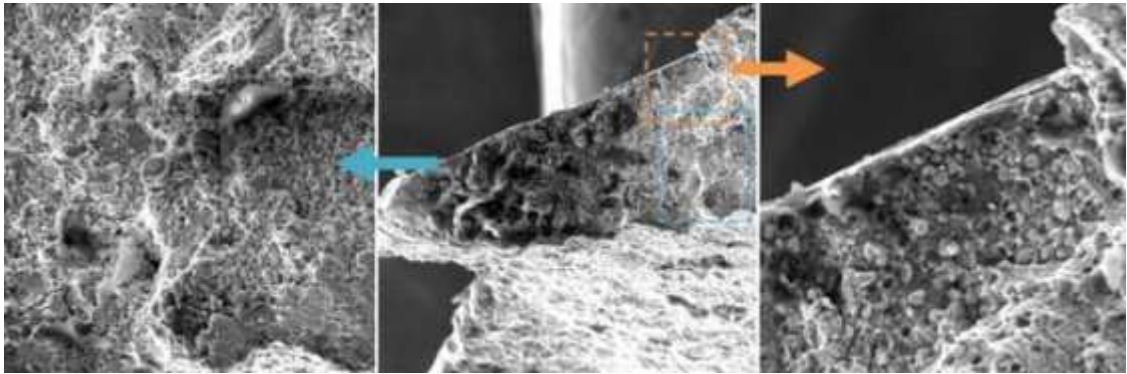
Злам 2. Поверхня зовнішньої обойми підшипника № 7
